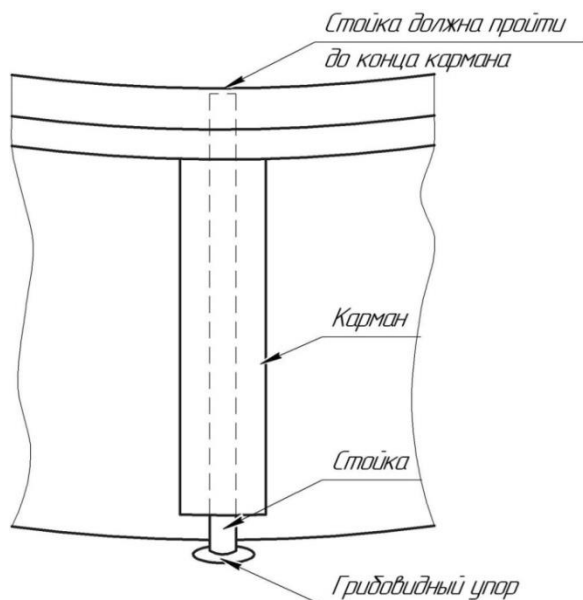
Схема сборки бака ЕКУД для воды
